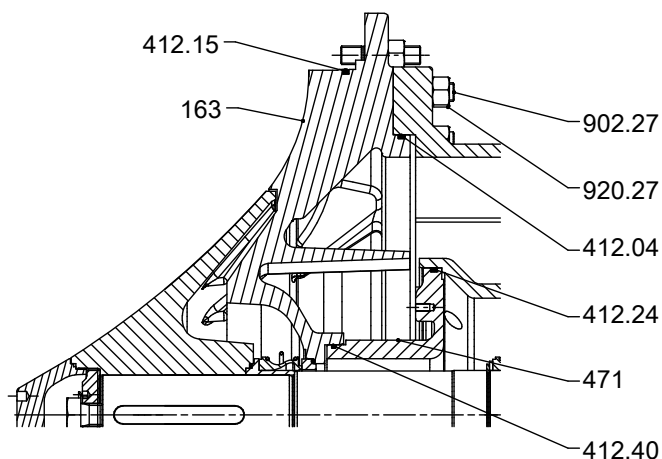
Besonderheit Hydraulik - Pumpenaggregat ohne Kühlsystem
